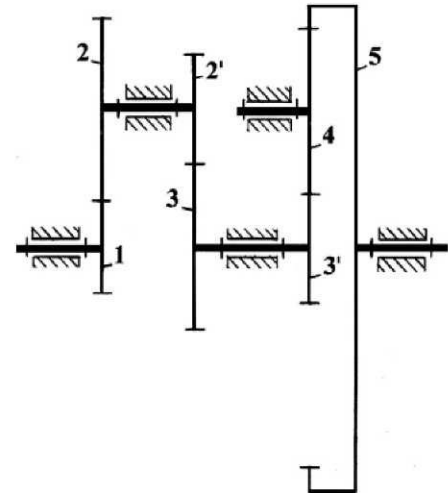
Многоступенчатый зубчатый механизм
